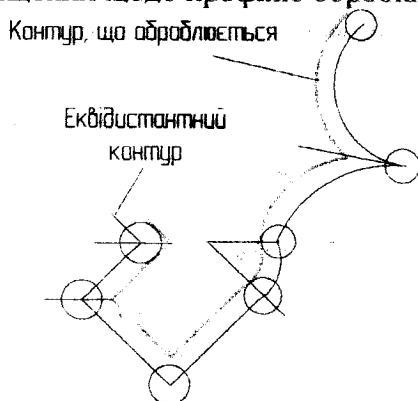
Положення інструмента в точках з'єднання контуру
